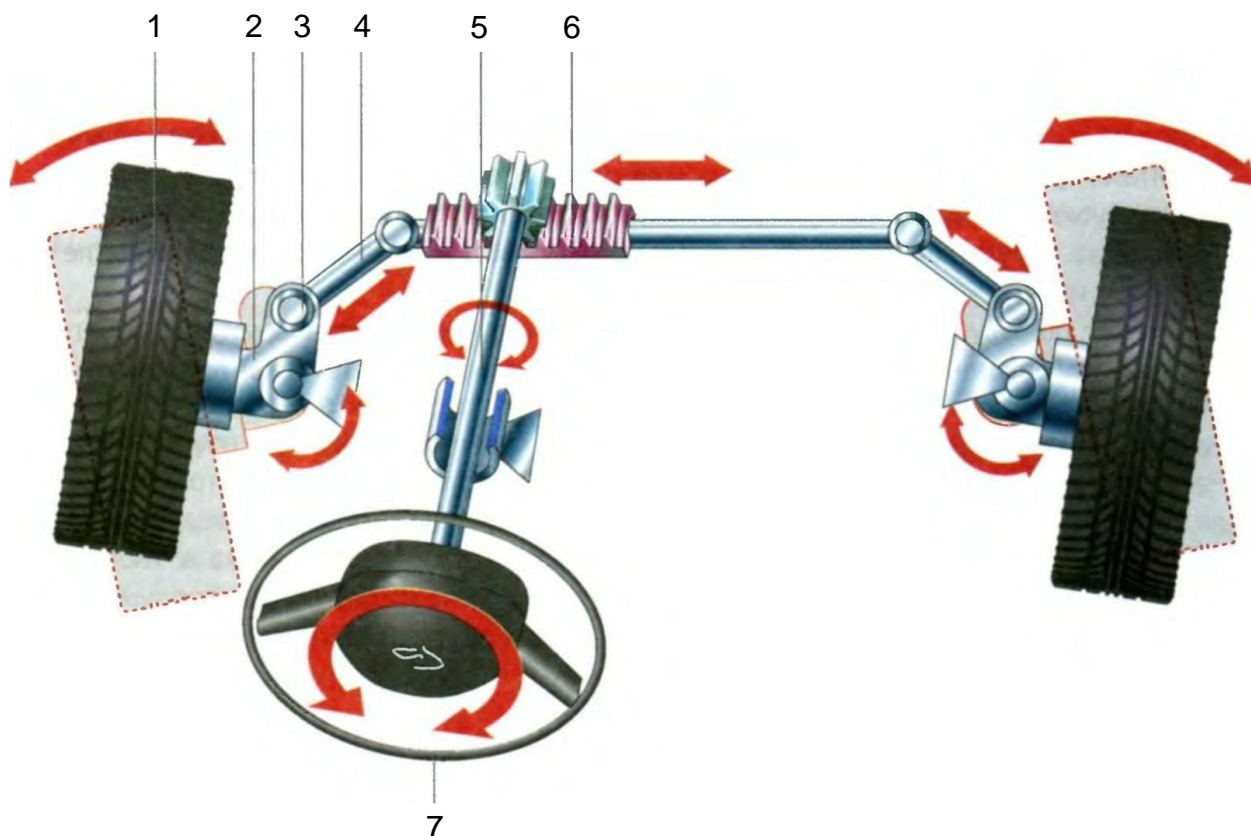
Схеми роботи рульового керування типу «шестерня – рейка»:
